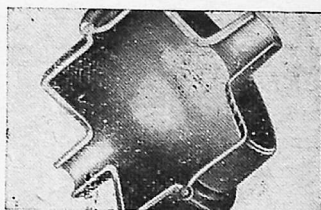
Вакуумная газодуговая сварка алюминия с отбортовкой (разрез).
